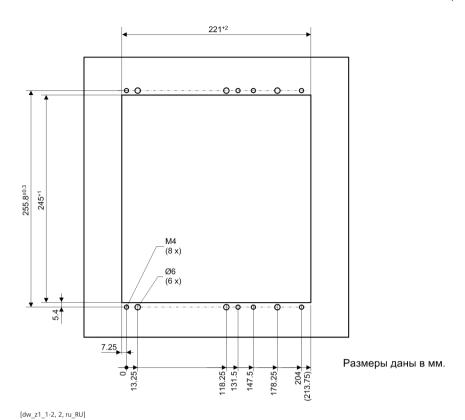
Ширина вырезов и схема сверления отверстий – устройство 1/2, первый ряд устройств
